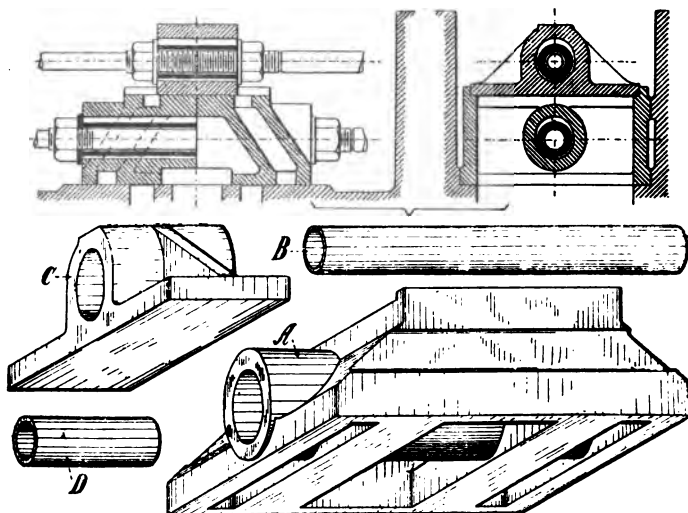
357. Teile zur Doppelschiebersteuerung mit fixer Expansion.
